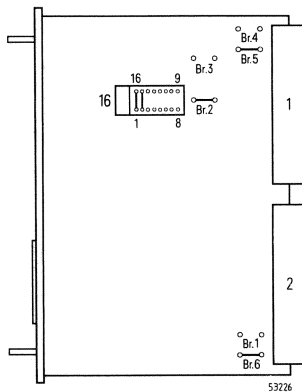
Zentralbaugruppe 6ES5 926-3, Einbaulage der Brücken
